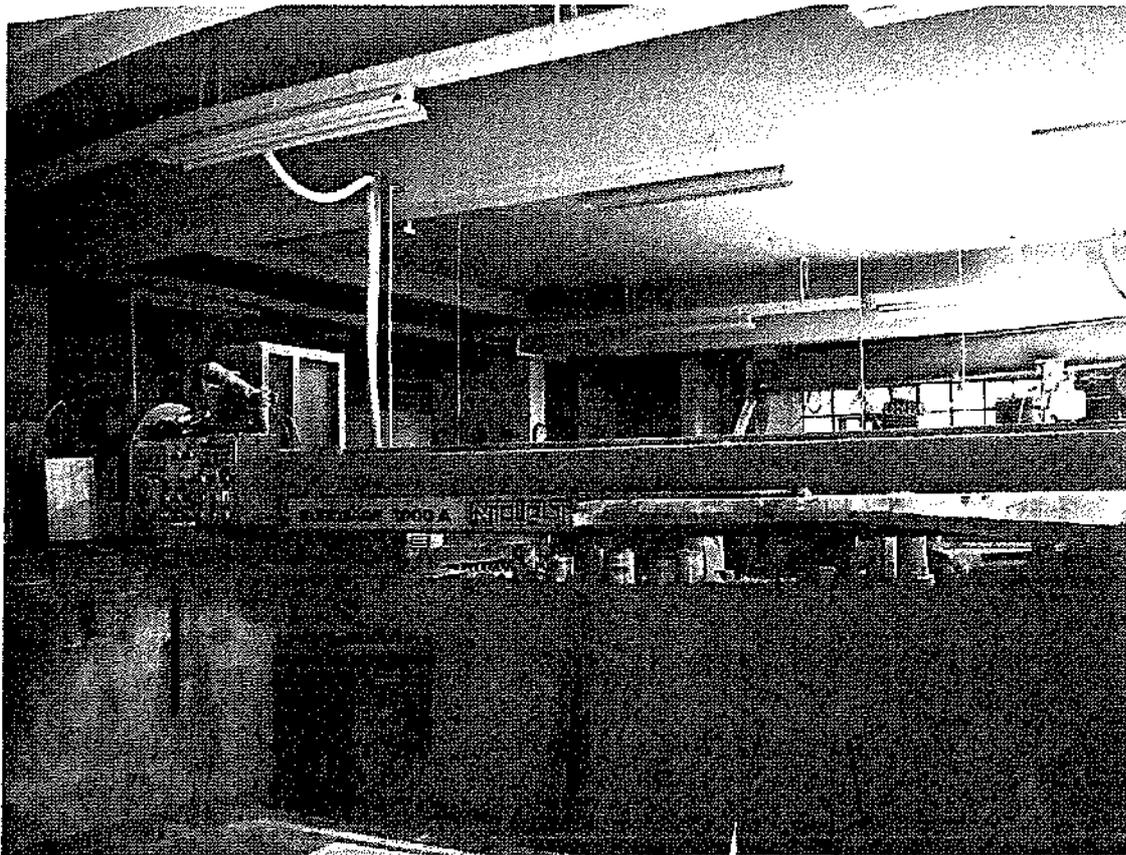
Lotto 7 – Interno del laboratorio per lavorazione marmi, ubicato al piano seminterrato.
